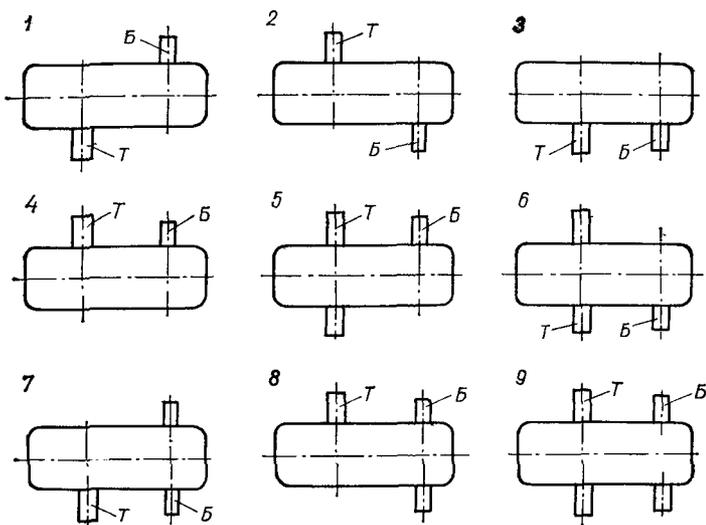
Схемы сборок (1—9) редуктора ЦОМ-30:
